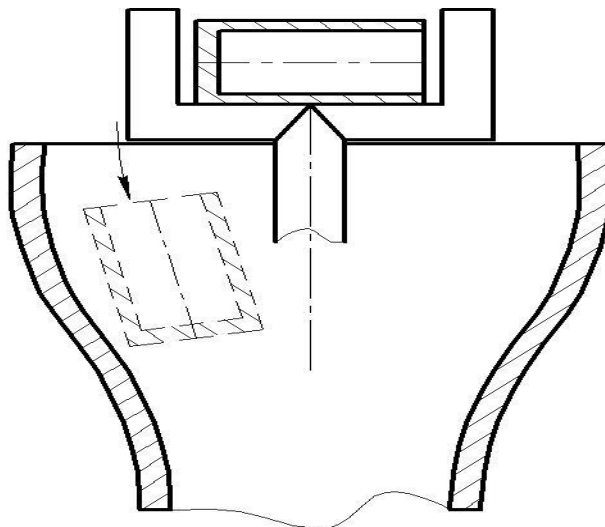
Схема орієнтування заготовки деталі за допомогою пристрою активної орієнтації – калібру ваги
